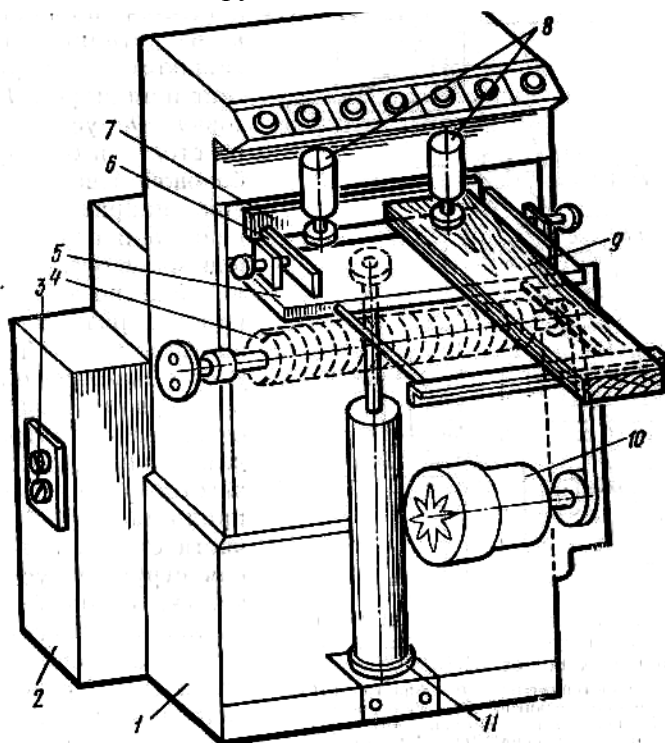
Станок шипорезный односторонний для прямого и клинового шипа:
